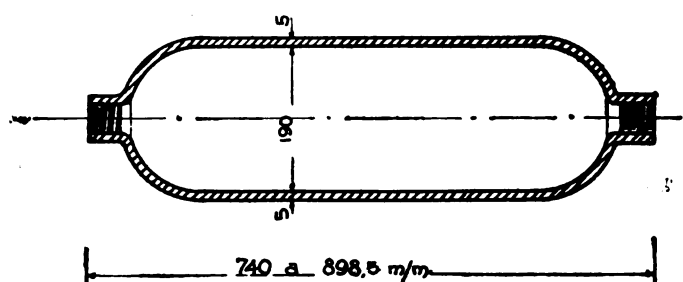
Sezione longitudinale di un cilindro di acciaio speciale per trasporto di gas ad alta pressione.
